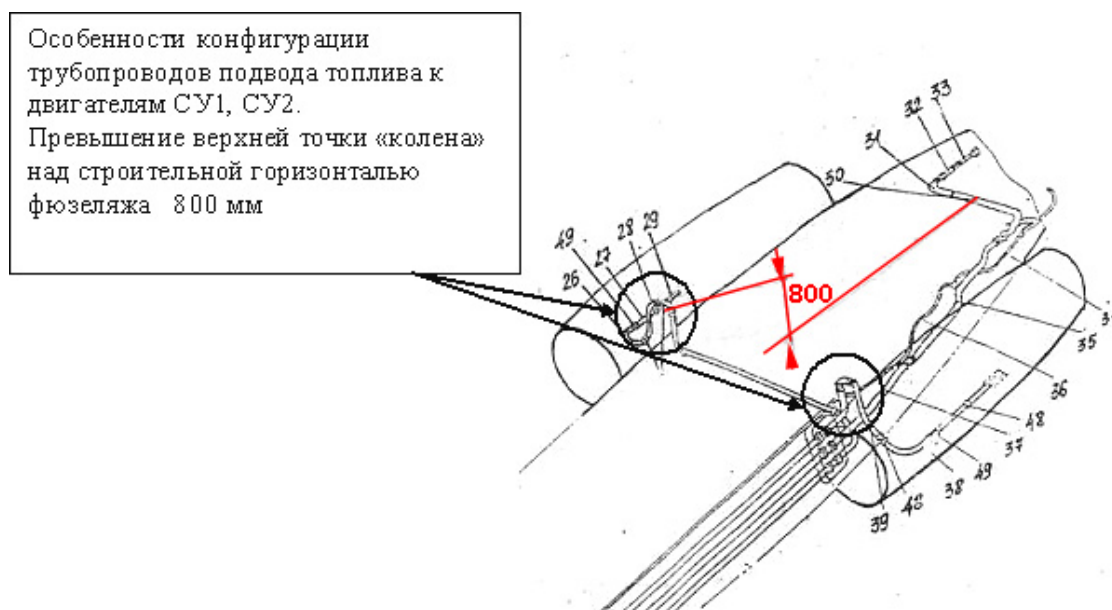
Схема прокладки топливных трубопроводов к двигателям самолета Ту-154М
